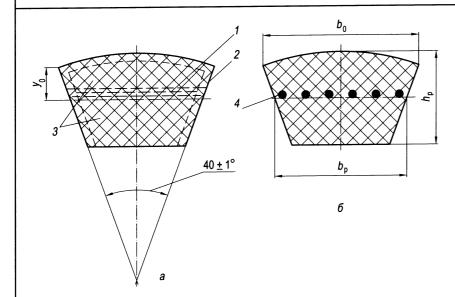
Сечения клинового ремня кордтканевого (a) и кордшнурового (b): 1- слой кордткани (бельтинга); 2- обкладка; 3- резиновая масса; 4- кордшнуры
